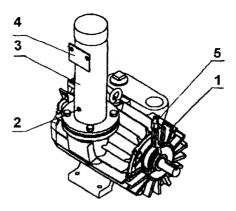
Схема расположения точек смазки пластинчатого вакуумного насоса:
